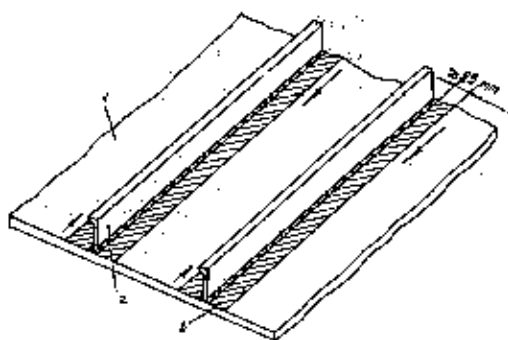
Схема упрочнения околошовной зоны приварки набора к полотнищу секции корпуса судна:
